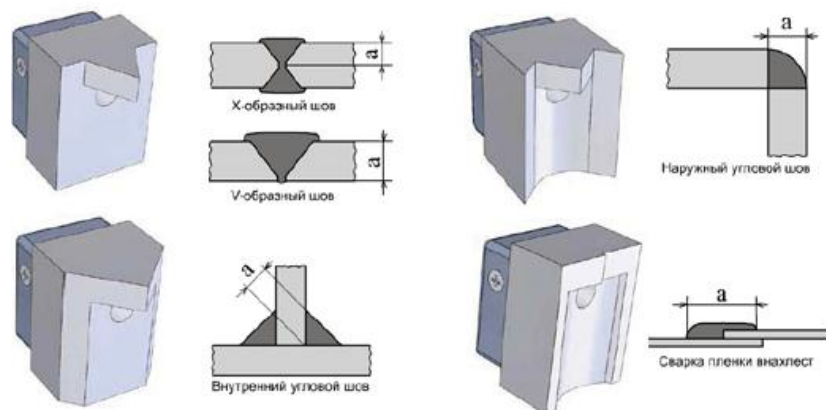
Формы сварочных башмаков и сварных швов
